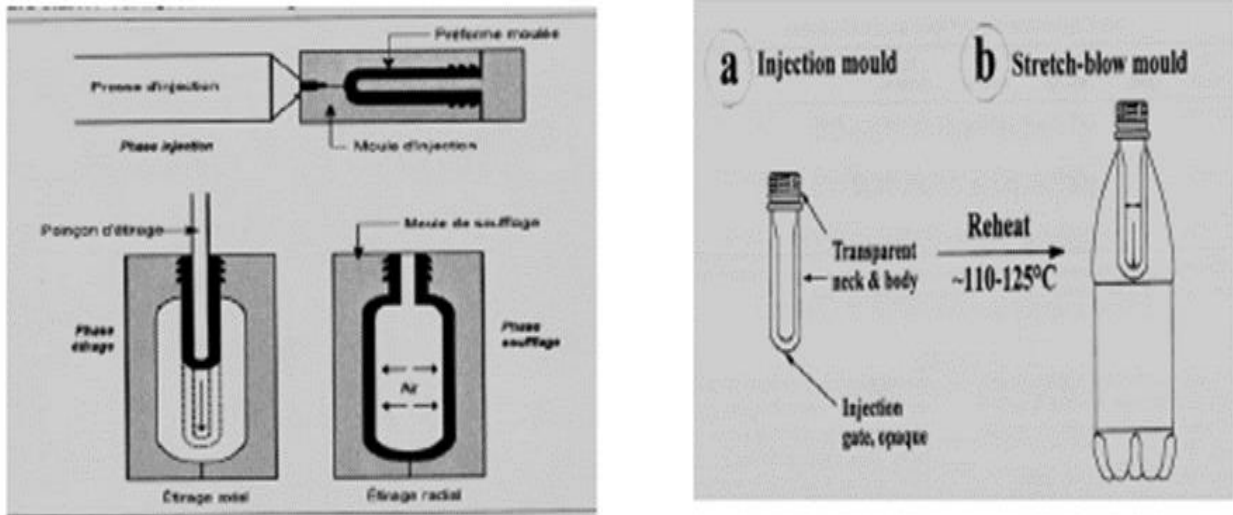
Procédé d'injection d'une préforme et de soufflage (bi-étirage) de la bouteille PET [33]
